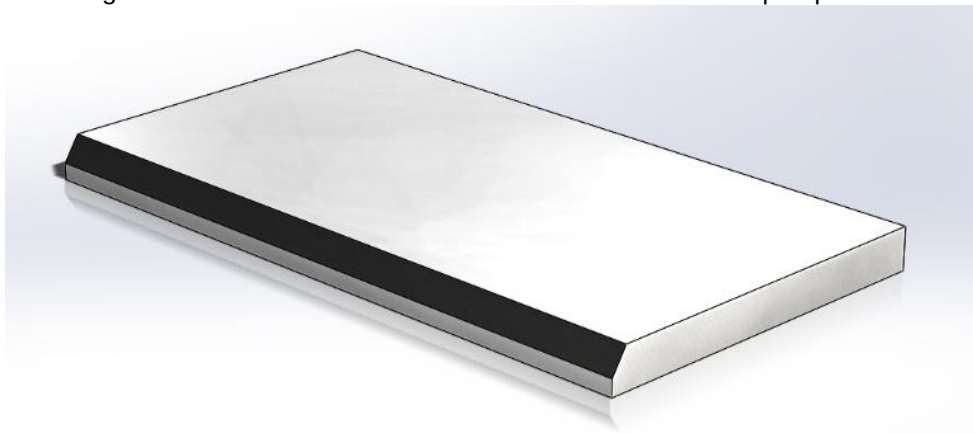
, mostra o desenho do conjunto soldado juntando as duas peças.
